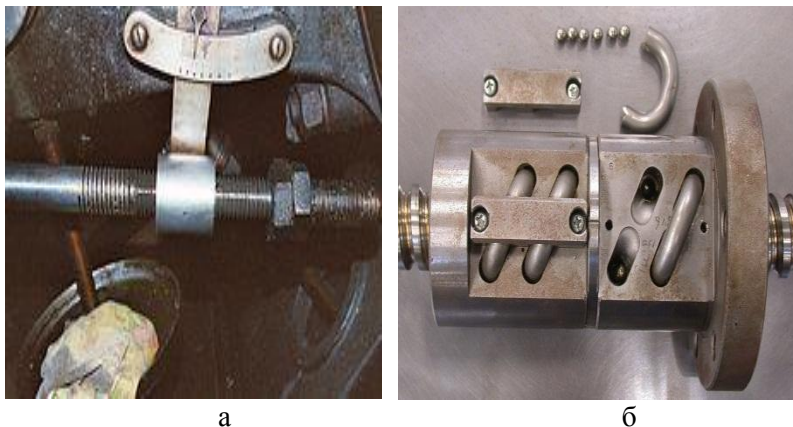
Конструкції: а – передача ковзання, гвинт-гайка, б – кулькова передача
